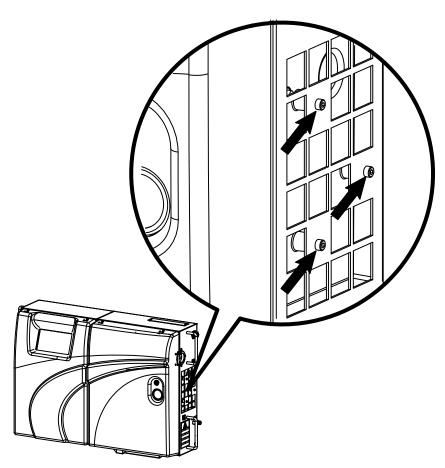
Position der Schrauben, die die Baugruppe Pneumatiksteuerung befestigen
